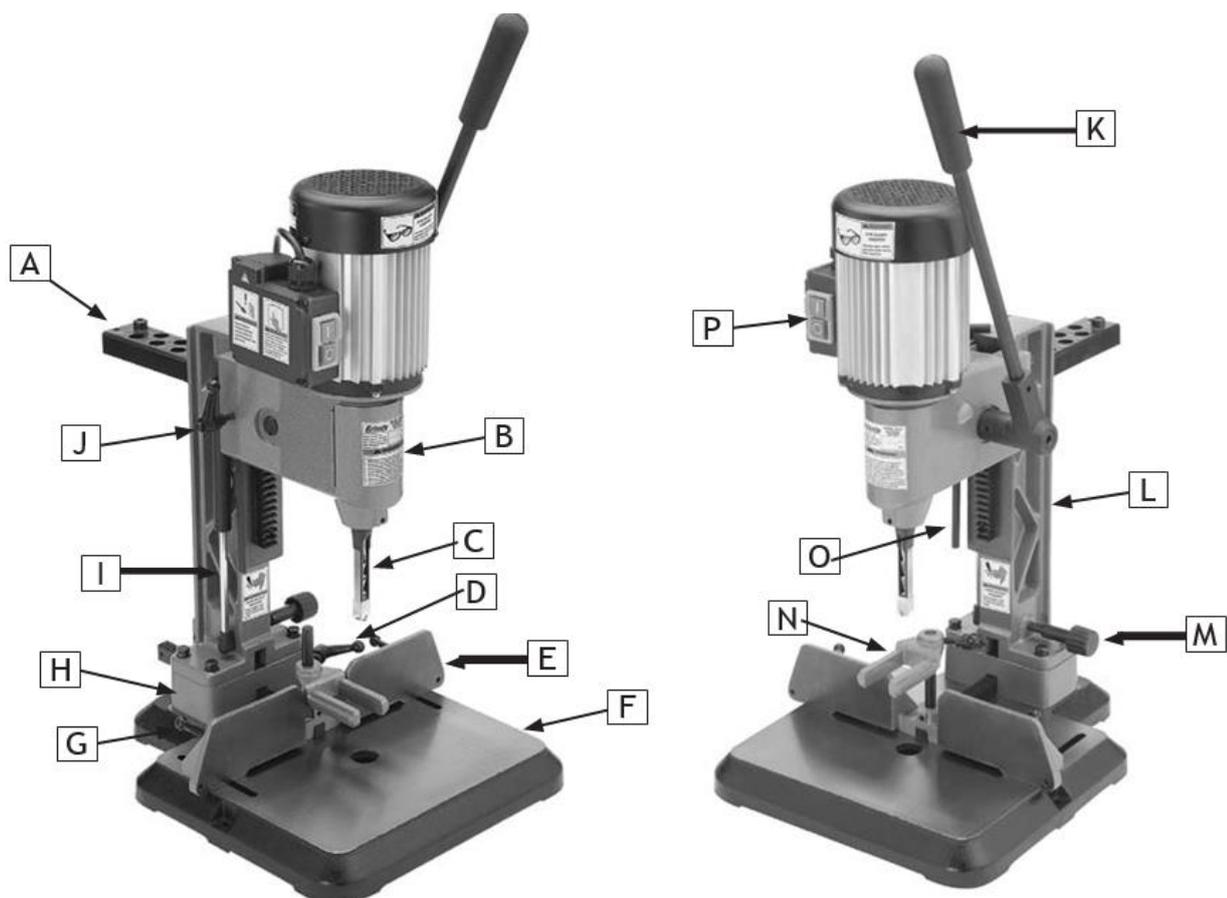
Основные элементы сверлильно-долбежного станка JIB MS3-8.
